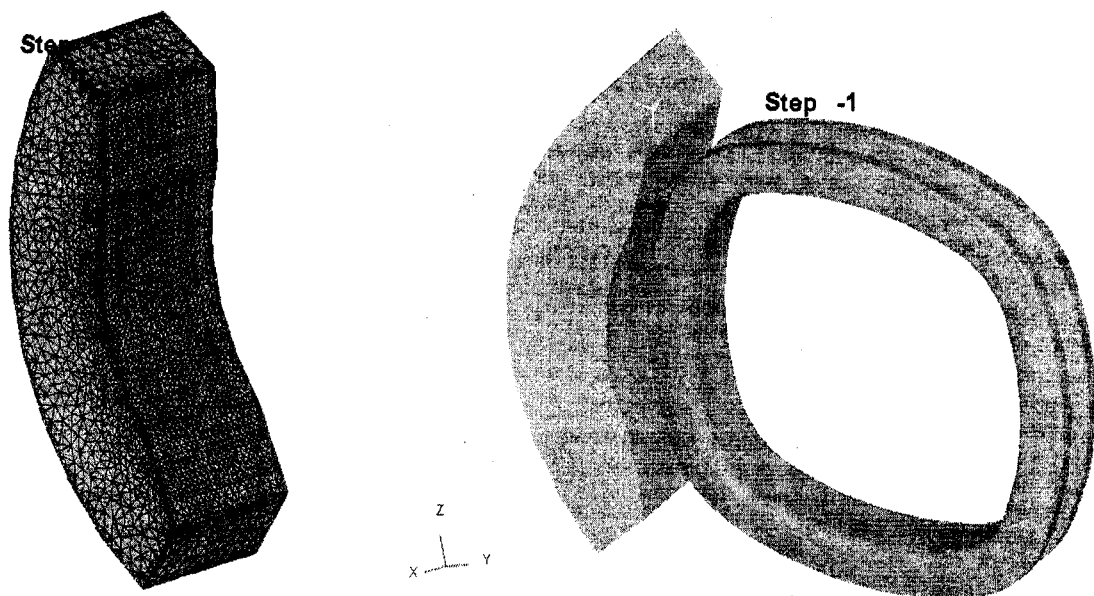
Геометрическая модель заготовки и инструмента в системе DEFORM
